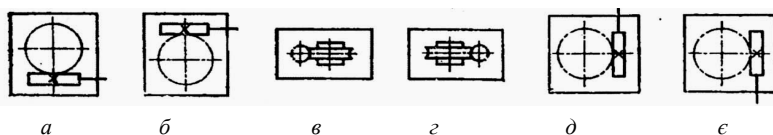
Схеми варіантів розміщення черв'ячної пари редукторів типу Ч:
